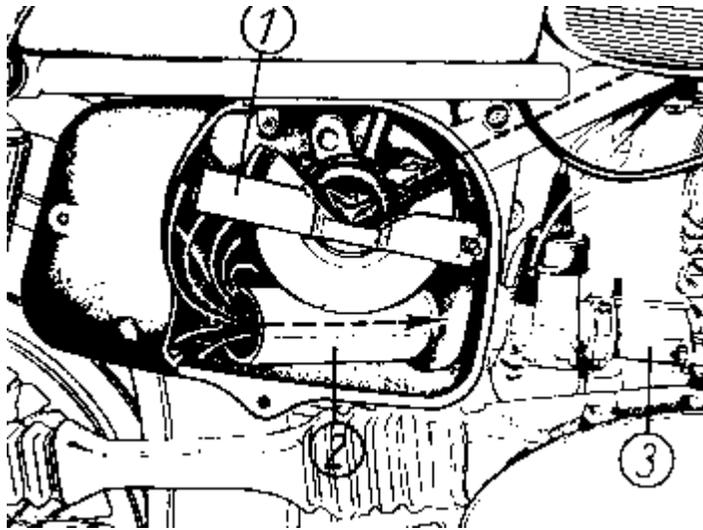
Ansaugeräuschkämpfer mit Filteranlage, Filtereinsatz aufgeschnitten
